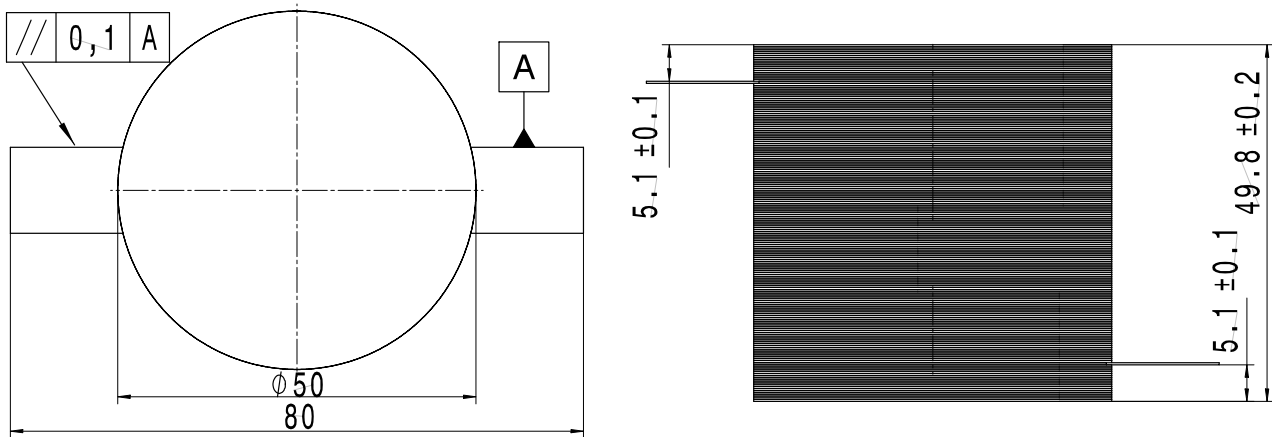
Blechpaket: Zusammenbauzeichnung der Druck-Torsionsprüflinge.
